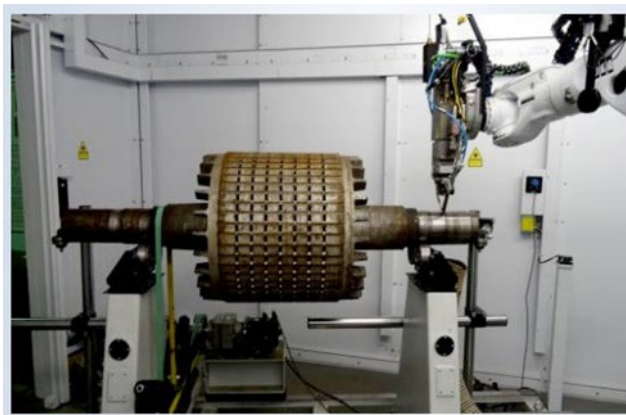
Внешний вид ротора электрического двигателя насоса
